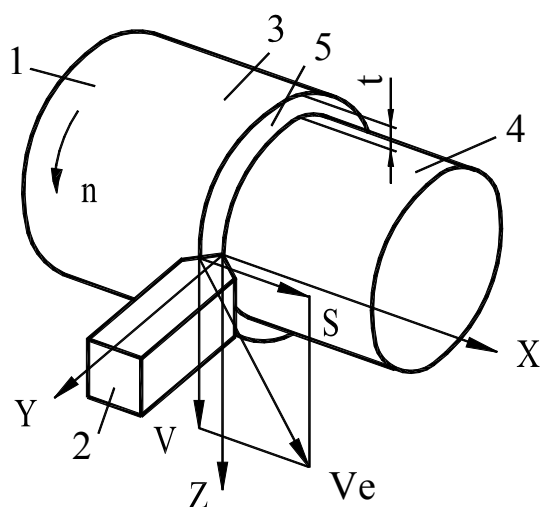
Кинематическая схема продольного точения [42]: 1 – заготовка, 2 – резец, 3 – обрабатываемая поверхность, 4 – обработанная поверхность, 5 – поверхность резания; n – угловая скорость заготовки; V – скорость резания, S – скорость движения подачи, V_e – результирующая скорость, t – глубина резания
